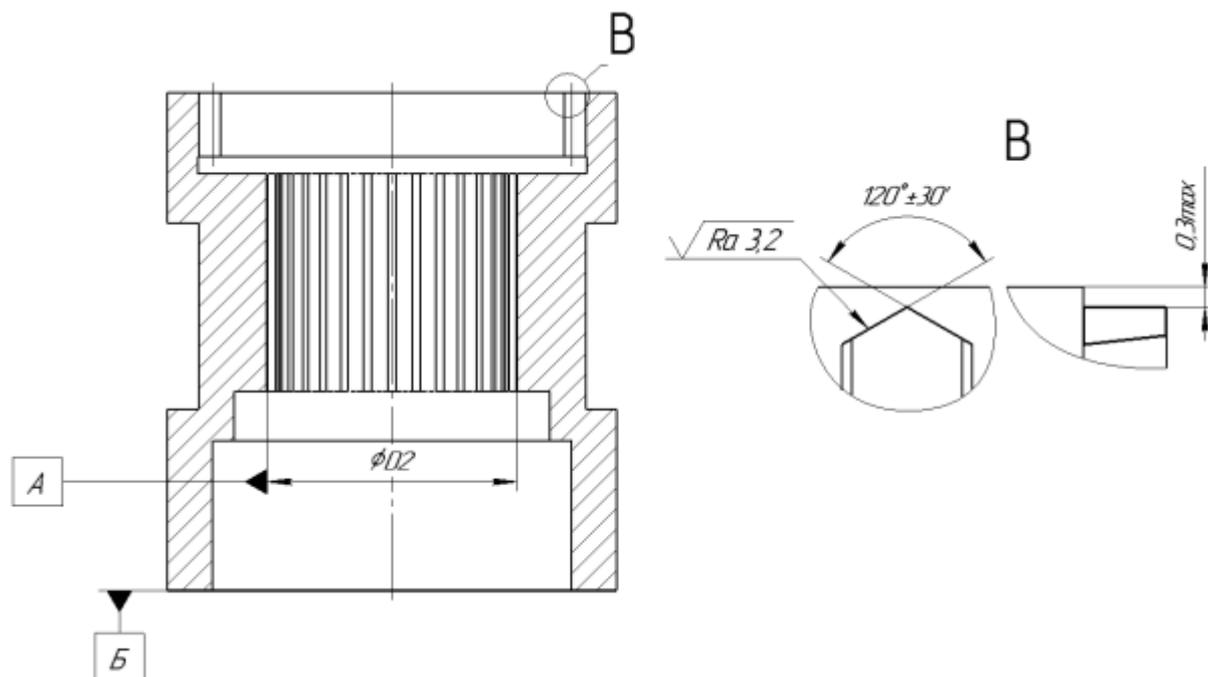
Эскиз обрабатываемой заготовки с указанием конструкторских баз
